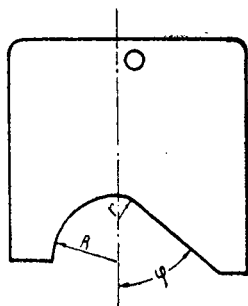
Шаблон для заправки шлифовального круга при шлифовке канавок метчиков.
